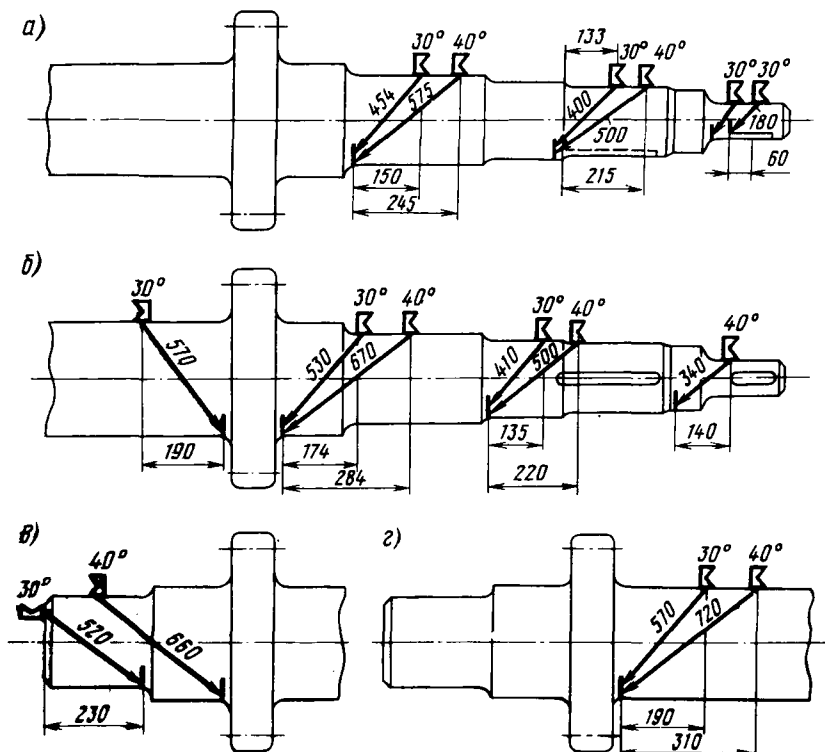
Схемы и зоны контроля наклонными искателями главного приводного вала эскалатора Н-10-20
